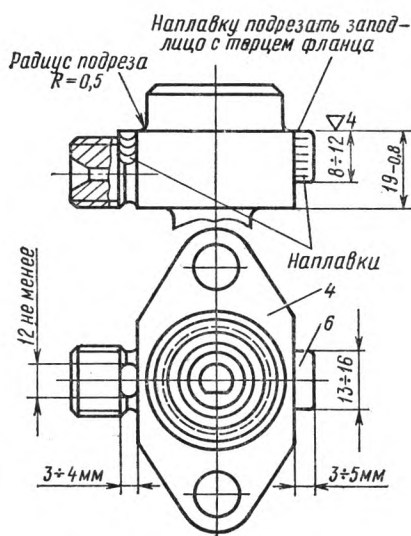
Изменение корпуса форсунки для закрепления нажимным фланцем (обозначения те же, что и на рис. 1)
